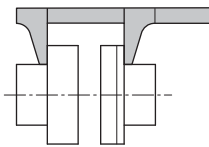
Проверка осевой выверки при помощи штангенциркуля
